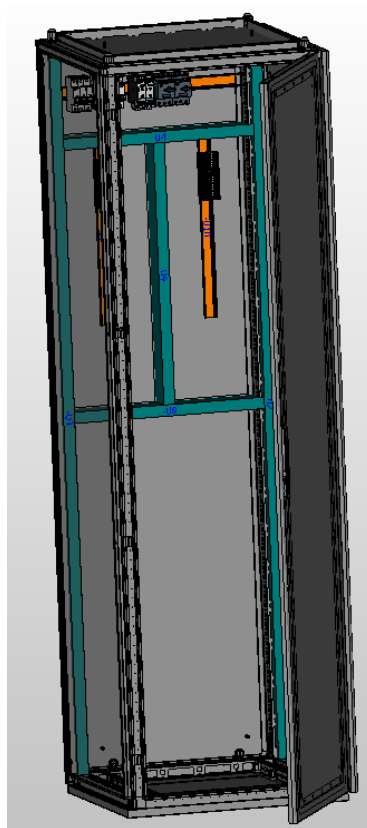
Загальний вигляд розробленої шафи для автоматизованого пристрою керування фонтаном
